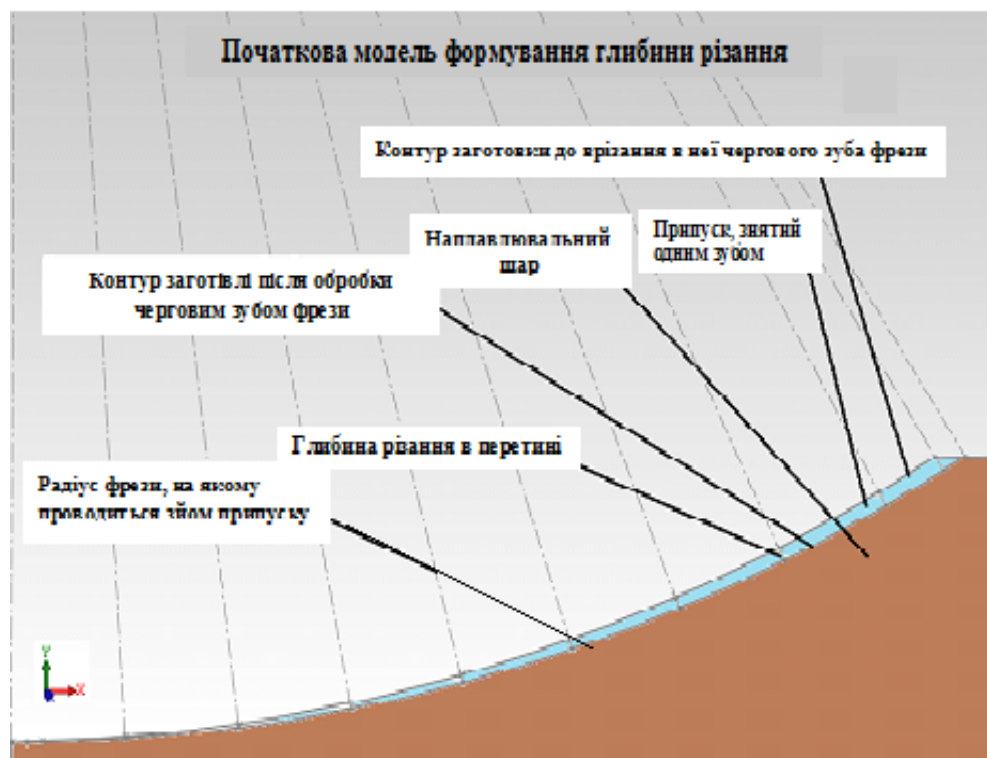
Початкова модель формування процесу формоутворення при відновленні крупногабаритних зубчастих коліс після наплавки
